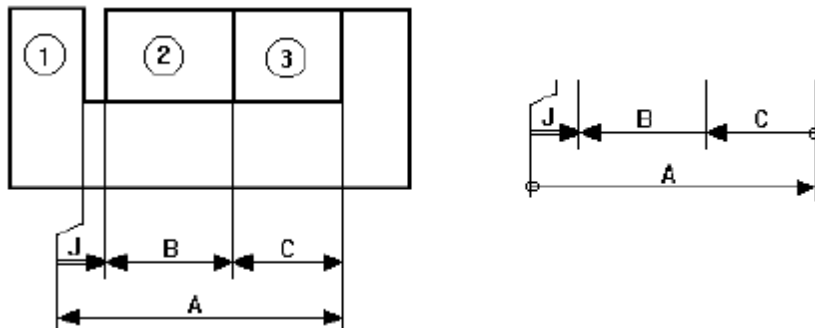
, representación de cadenas, Geometric dimensioning and tolerancing. The American Society of mechanical engineers. Norma ASME Y14-5. Dimensioning and tolerancing. 2009.
